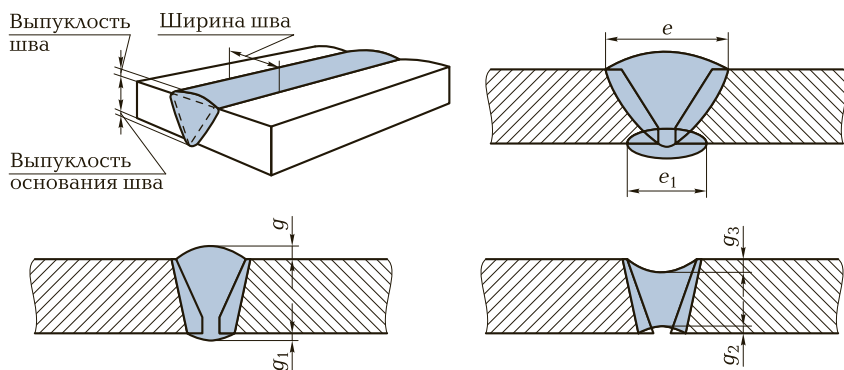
Конструктивные элементы стыкового сварного шва:
